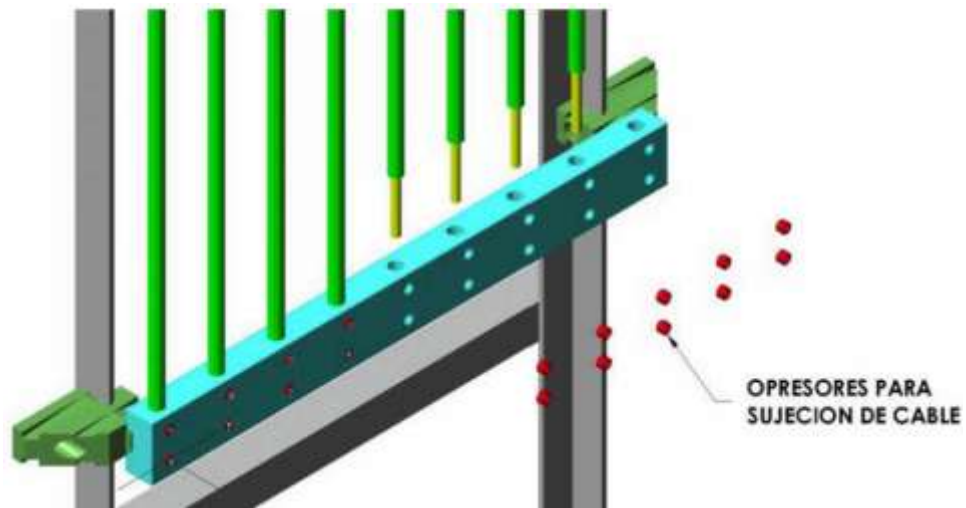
Conexión de los cableados en las barras de acero galvanizado BT2G12C.
